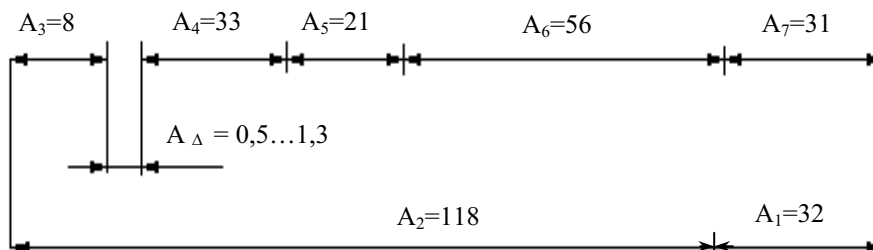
Схема размерной цепи с номинальными размерами, мм
